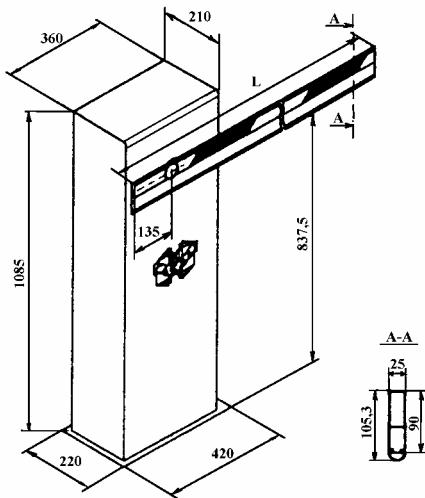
Габаритные размеры шлагбаума SPIN 3,4.
